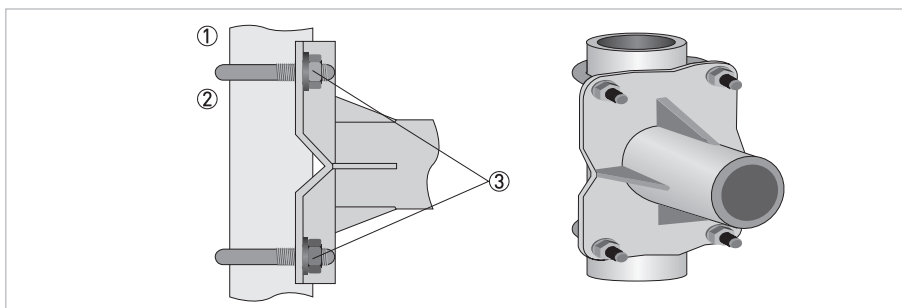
Крепление корпуса преобразователя сигналов полевого исполнения к трубе.
